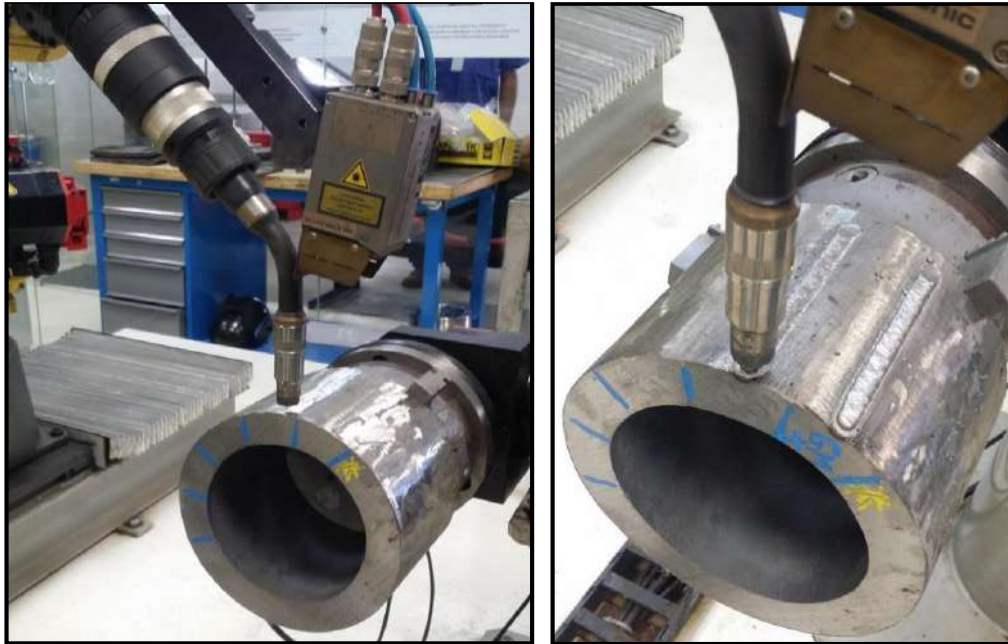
Soldagem GMAW com robô FANUC ARC Mate 120iC da empresa Lincoln Electric.
